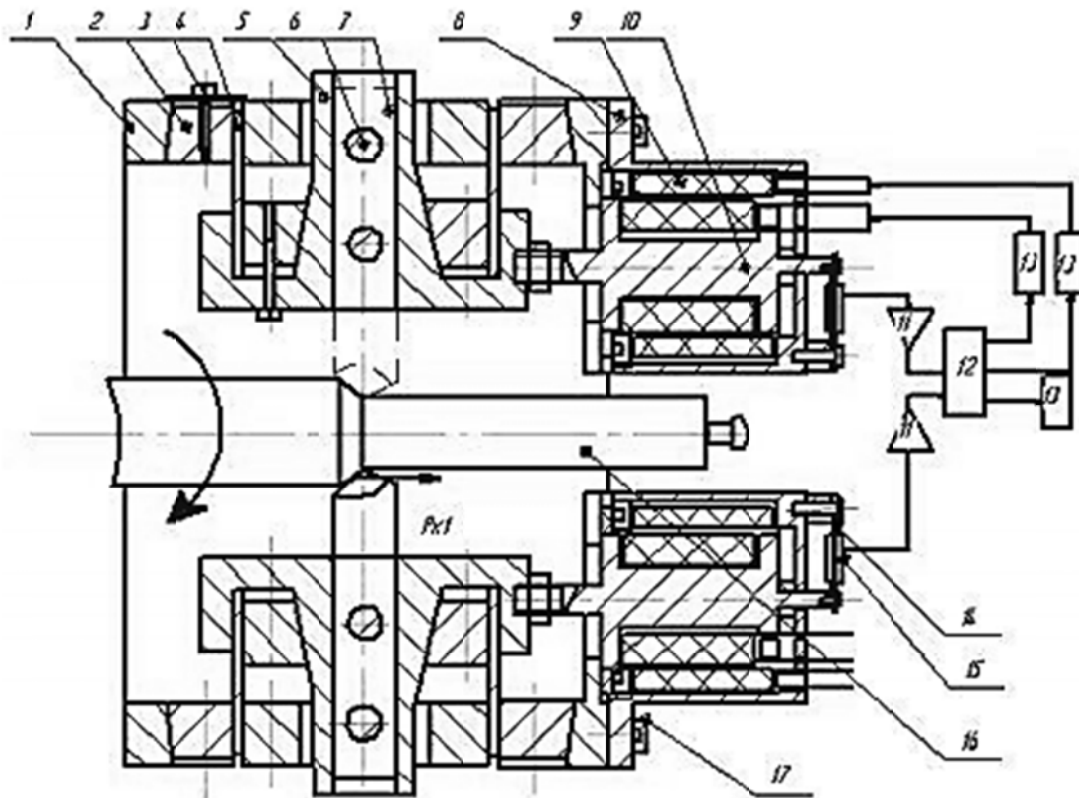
Конструкція багаторізцевої головки для тонкого точіння з пружними напрямними та електромагнітним приводом
